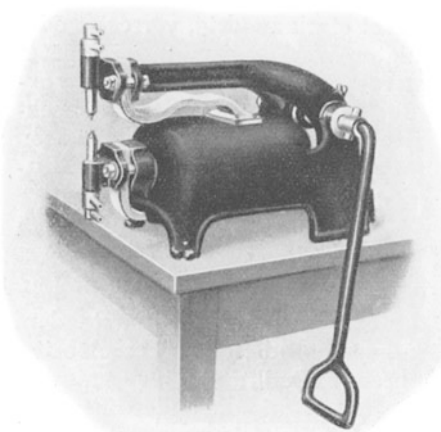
Tisch-Punktschweißmaschine.
